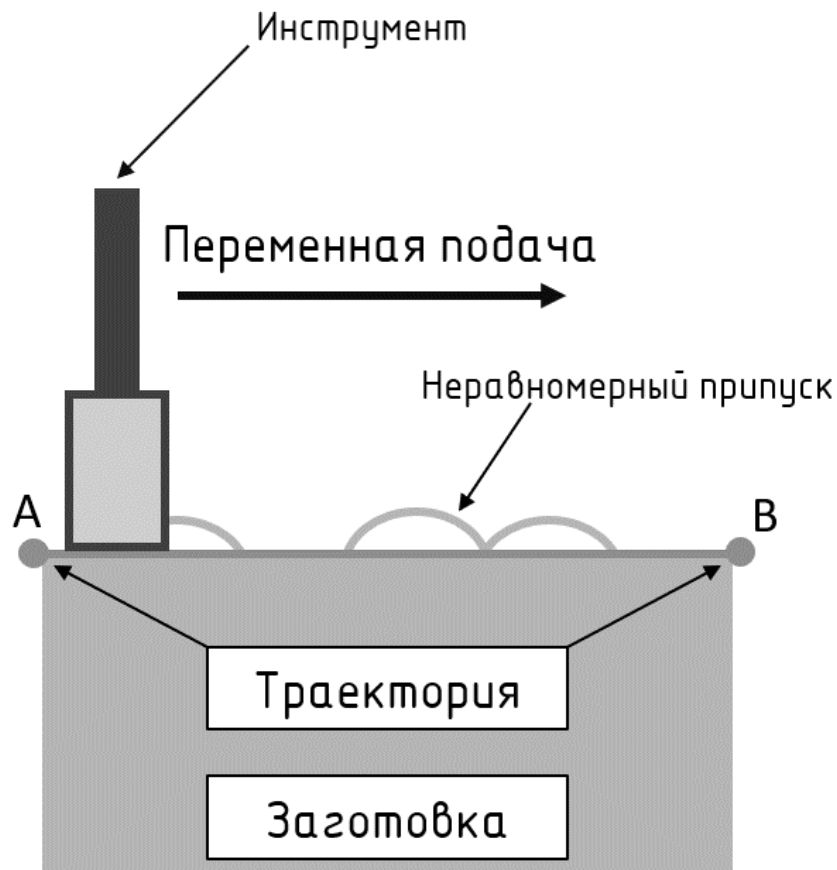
Обработка заготовки с неравномерным припуском
